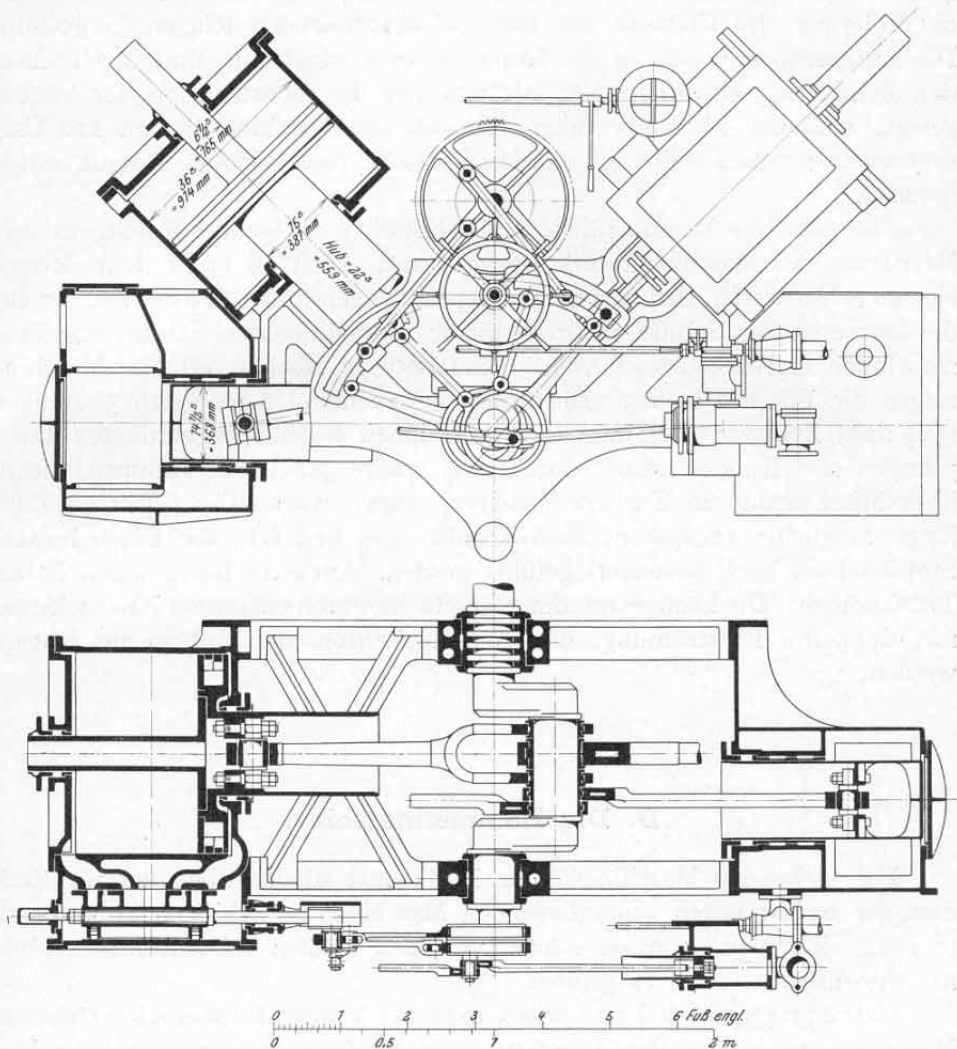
und 623. Schraubenschiffsmaschine von Tischbein in Buckau 1856.
